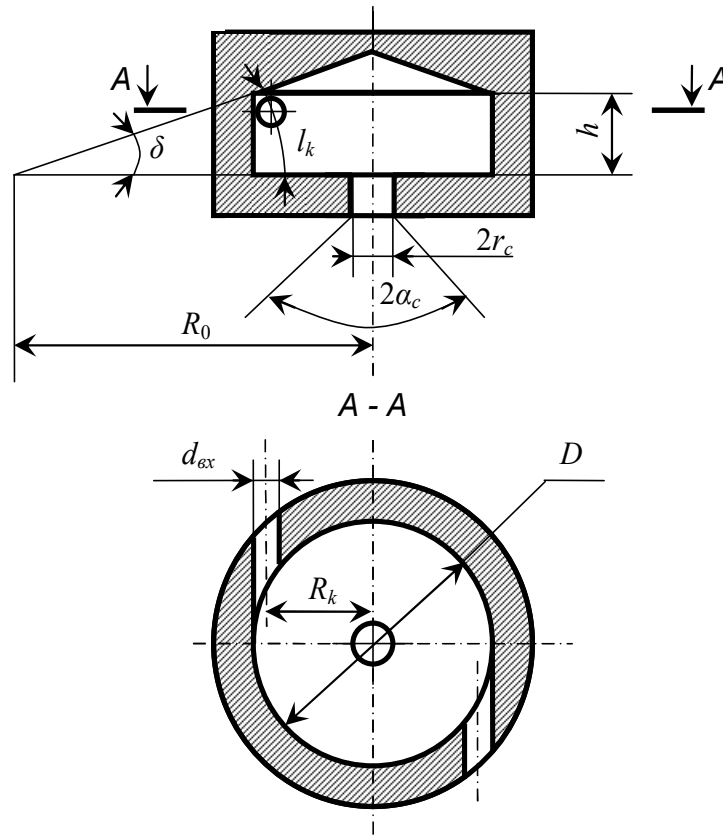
Схема камери закручування відцентрового розпилювача
